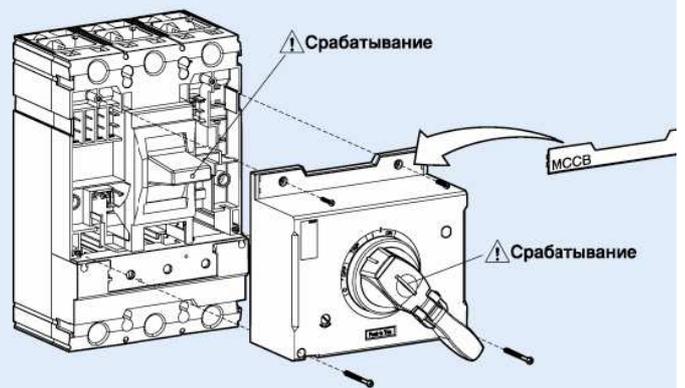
Габаритные и установочные размеры, способ установки стандартной поворотной рукоятки TS800
